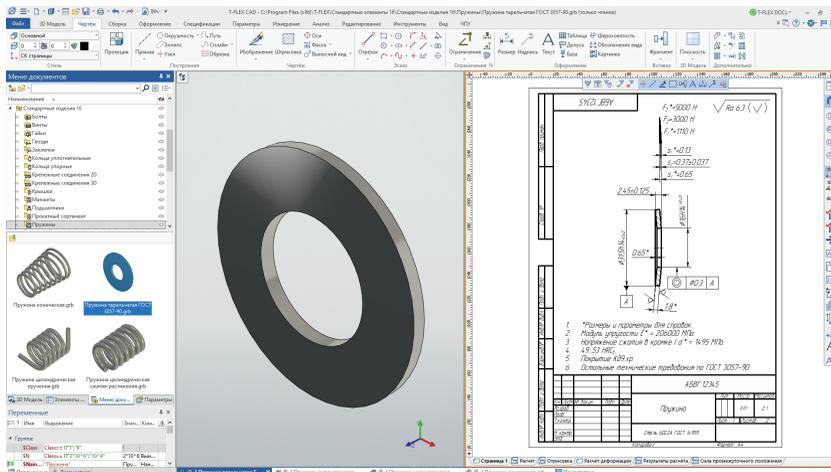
Тарельчатая пружина: 3D-модель и чертёж
